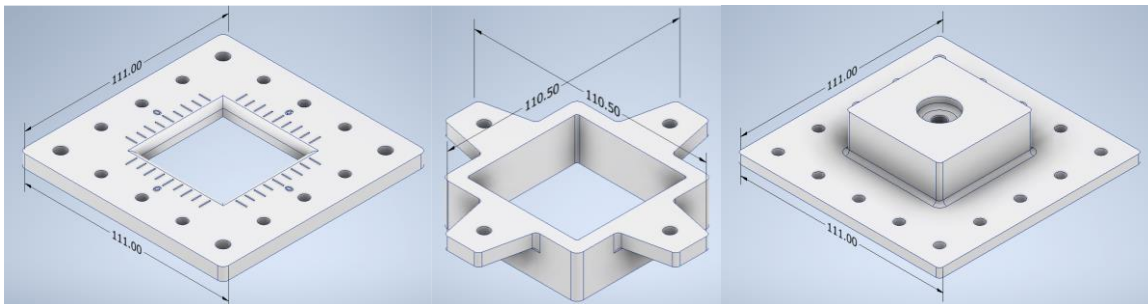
Piezas desarrolladas mediante software de CAD que conforman al receptor solar. De izquierda a derecha, las piezas son la tapa, cuerpo y base del receptor.
